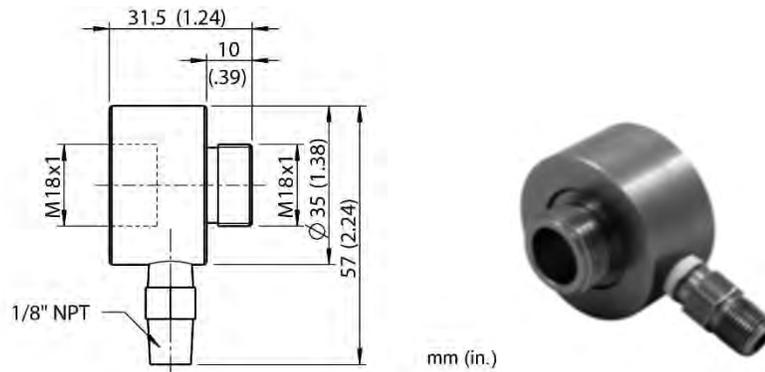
Dimensions du collier de soufflage d'air (XXXMI3100ADJB)
